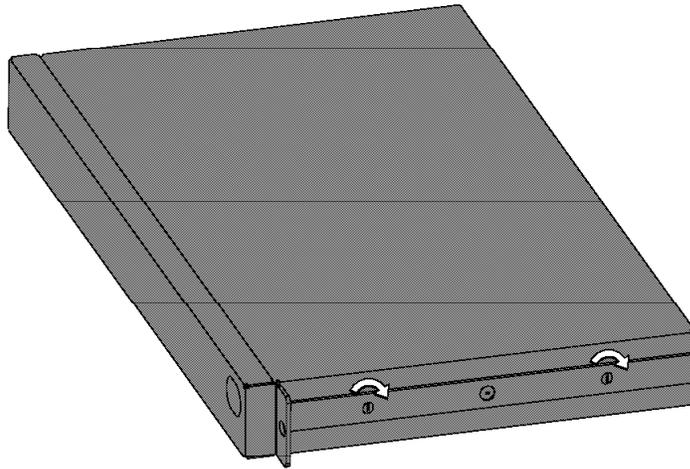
Reinstalação dos Parafusos e do Suporte de Montagem
